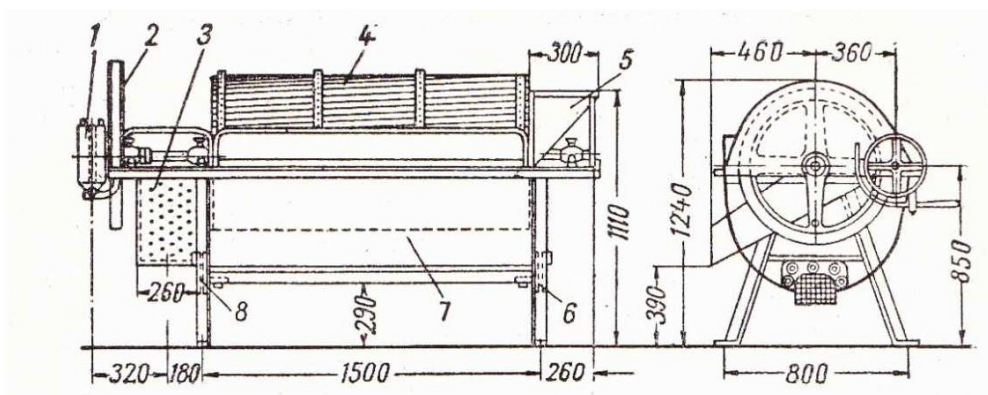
Схема барабанної коренебульбоплодної мийної машини безперервної дії: 1 - робочий і холостий шківи; 2 - передавальний механізм; 3 - випускний лоток; 4 - мийний барабан; 5 - завантажувальний лоток; 6, 8 - грязьові люки; 7 - корито для води
